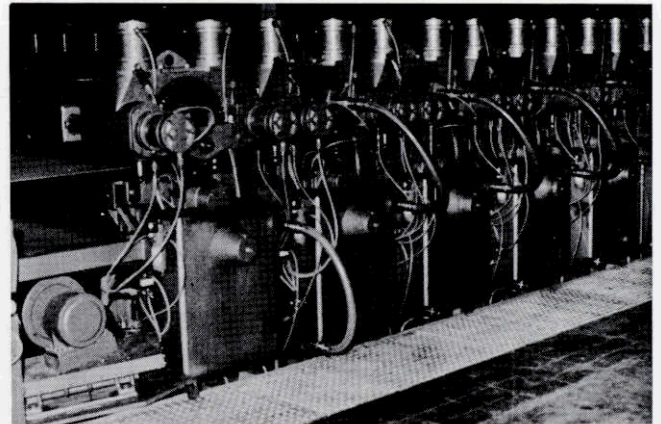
Rotations-Teppichdruckanlage, Gesamtansicht (Mitter & Co., Schloß Holte/BRD)
